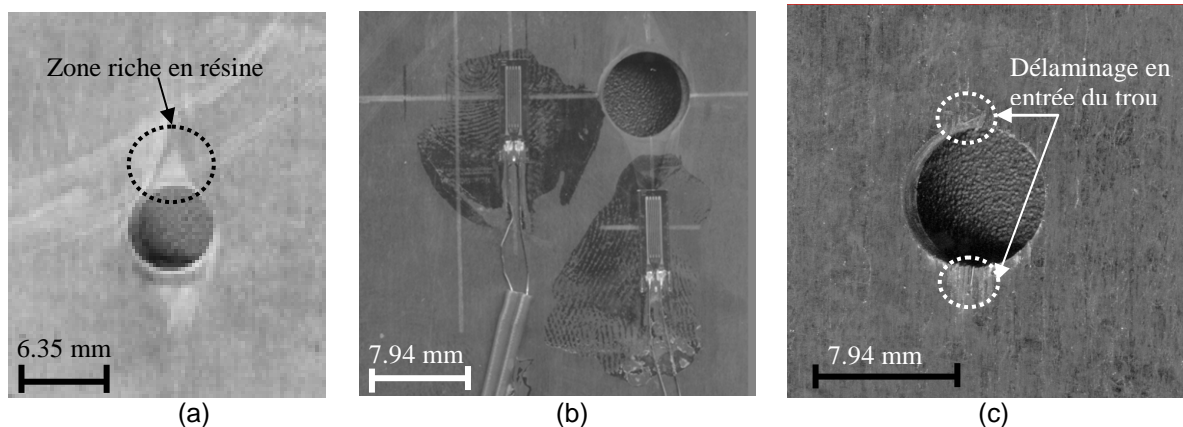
Images scannées, montrant l'état du trou ainsi que la position des jauges axiale et axiale décalée avec (a) éprouvette moulée de diamètre de 6,35 mm, (b) éprouvette moulée de diamètre de 7,94 mm et (c) éprouvette percée de diamètre 7,94 mm.
